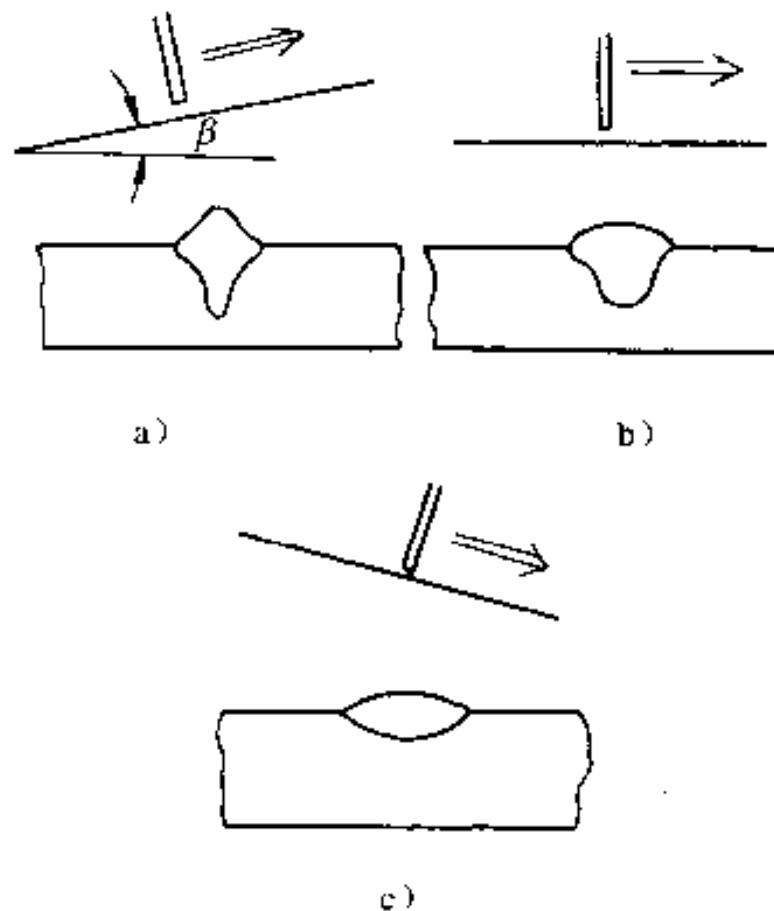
焊件倾斜对焊缝形状及尺寸的影响
